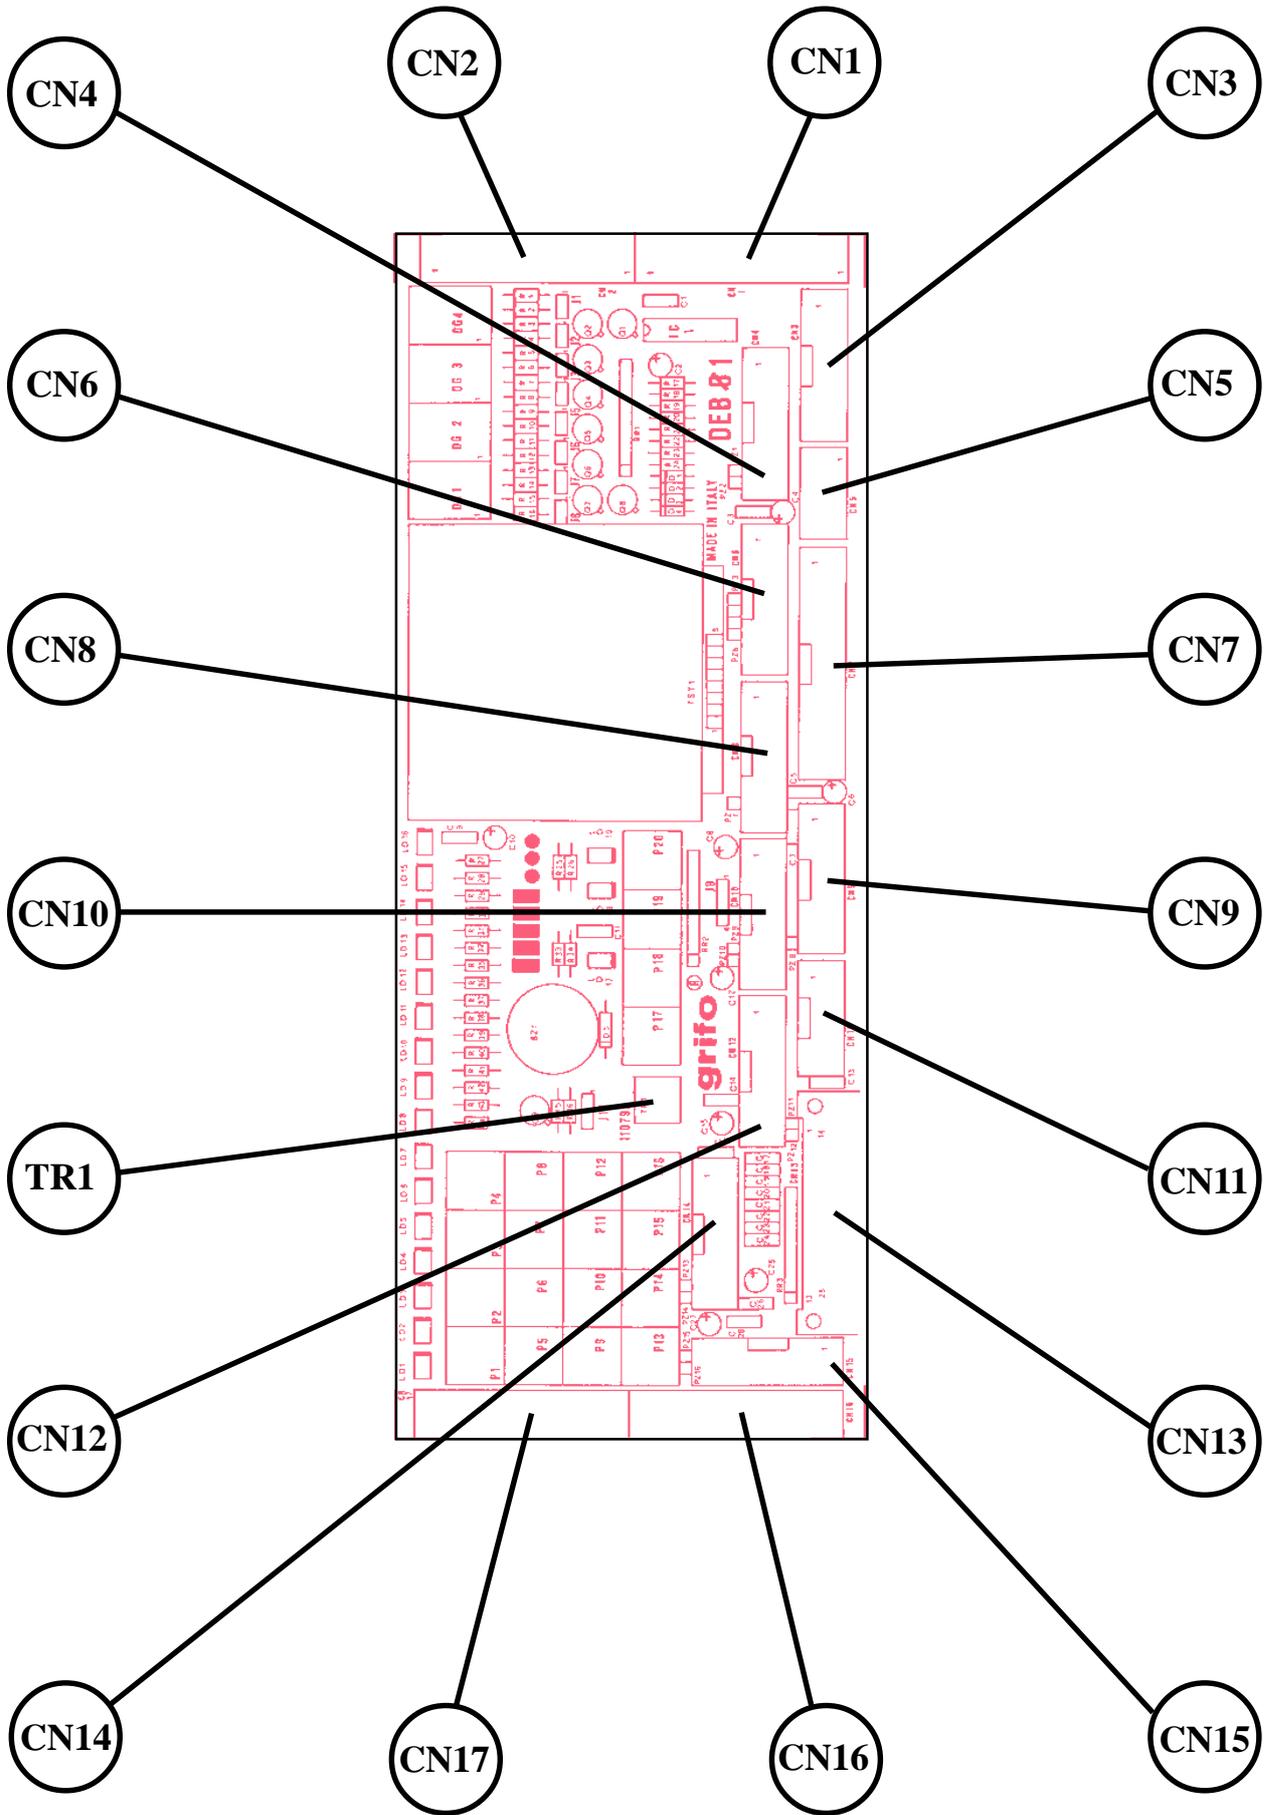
DISPOSIZIONE CONNETTORI E TRIMMER
